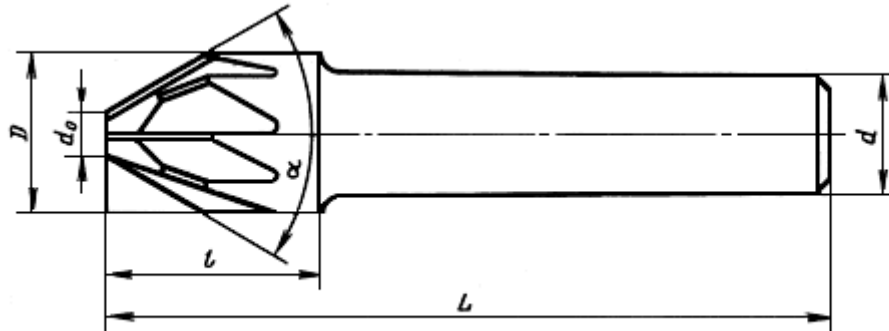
Зенківка 2353-0103 ГОСТ 14953-80
